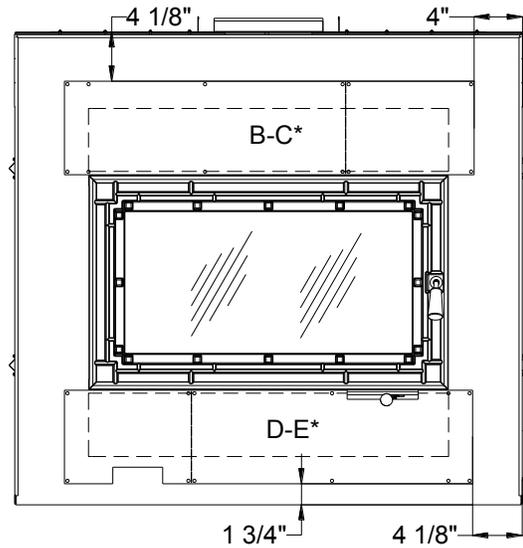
Installation des plaques d'obstruction sur un foyer Focus 320 ou Onyx2
